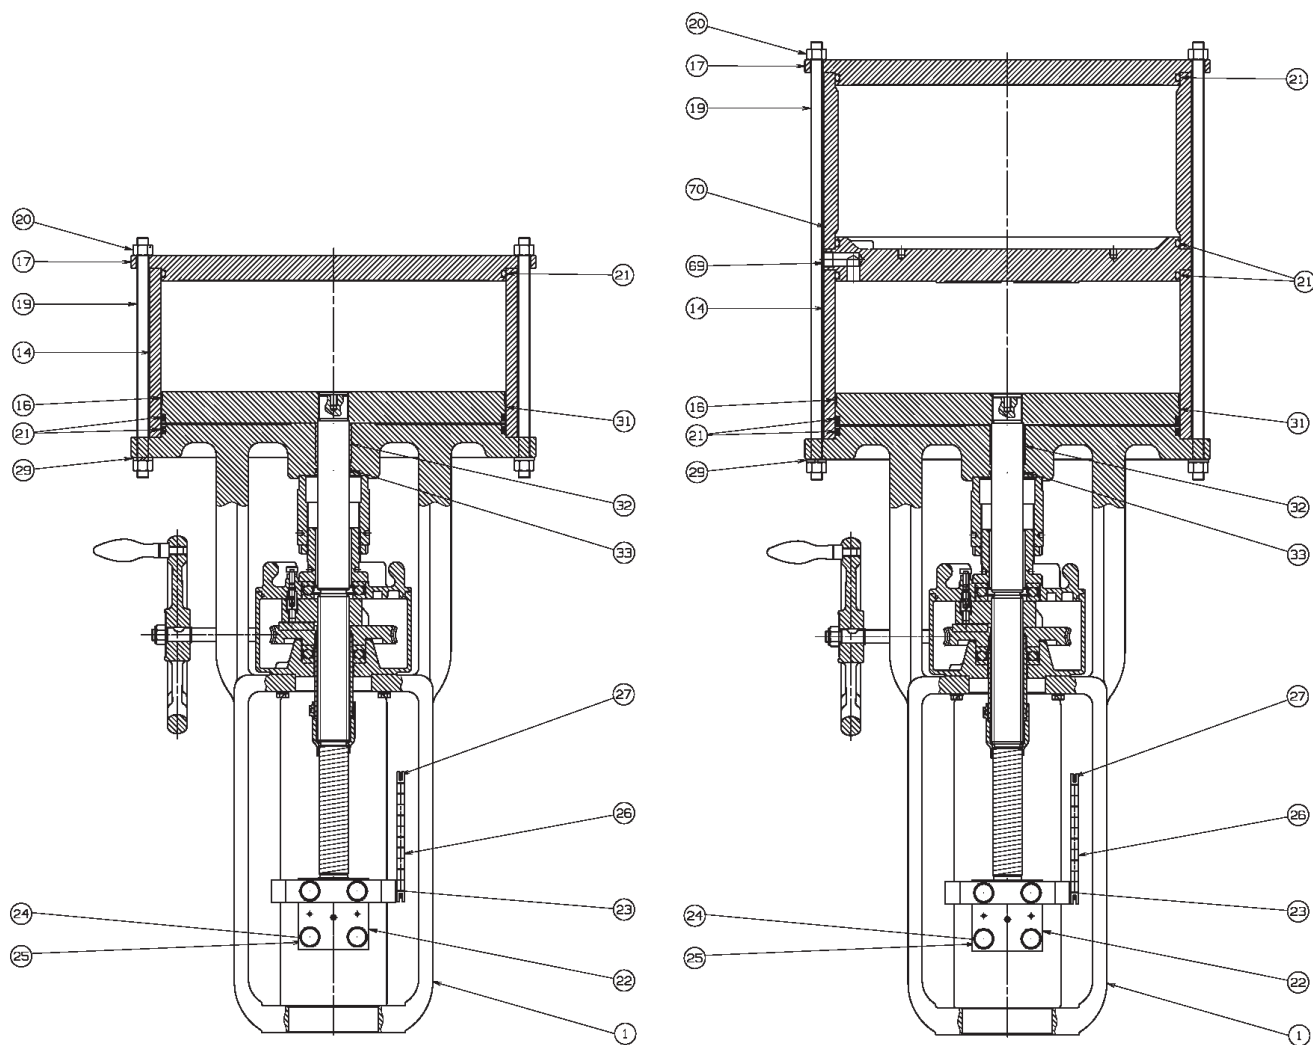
Модель 51 с маховиком, с резервуаром для сжатого воздуха и без резервуара
